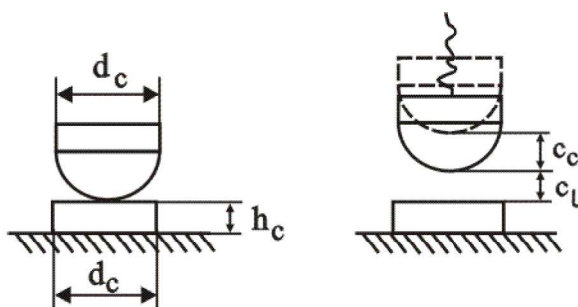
Explicativă la dimensionarea contactelor electrice
